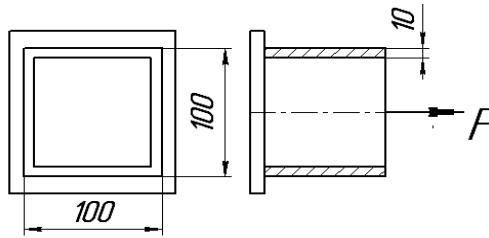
Сварное соединение, выполненное тавровыми сварными швами
